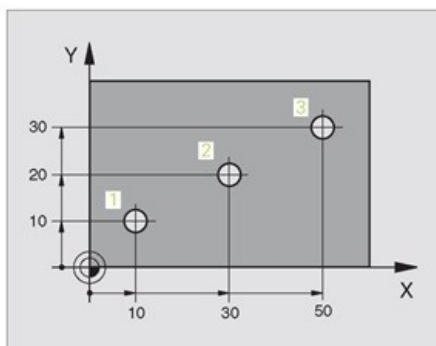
Definice kartézských souřadnic v pravotočivé soustavě [11]
